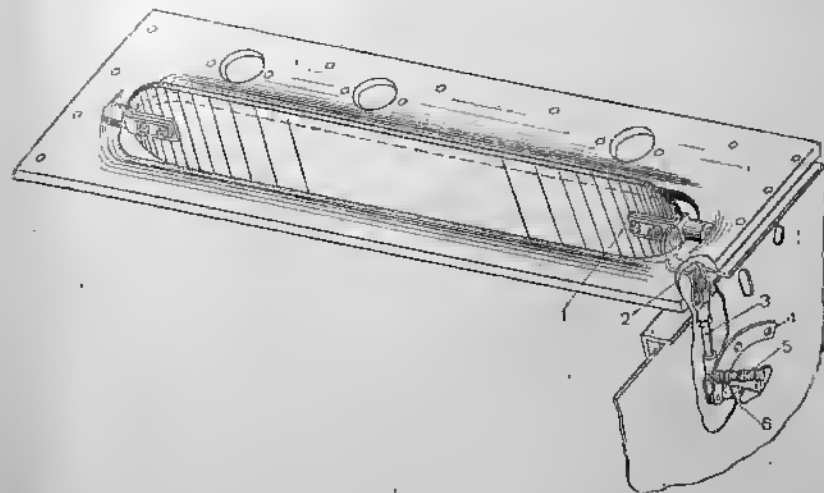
Привод жалюзи воздухопритока над радиатором:
